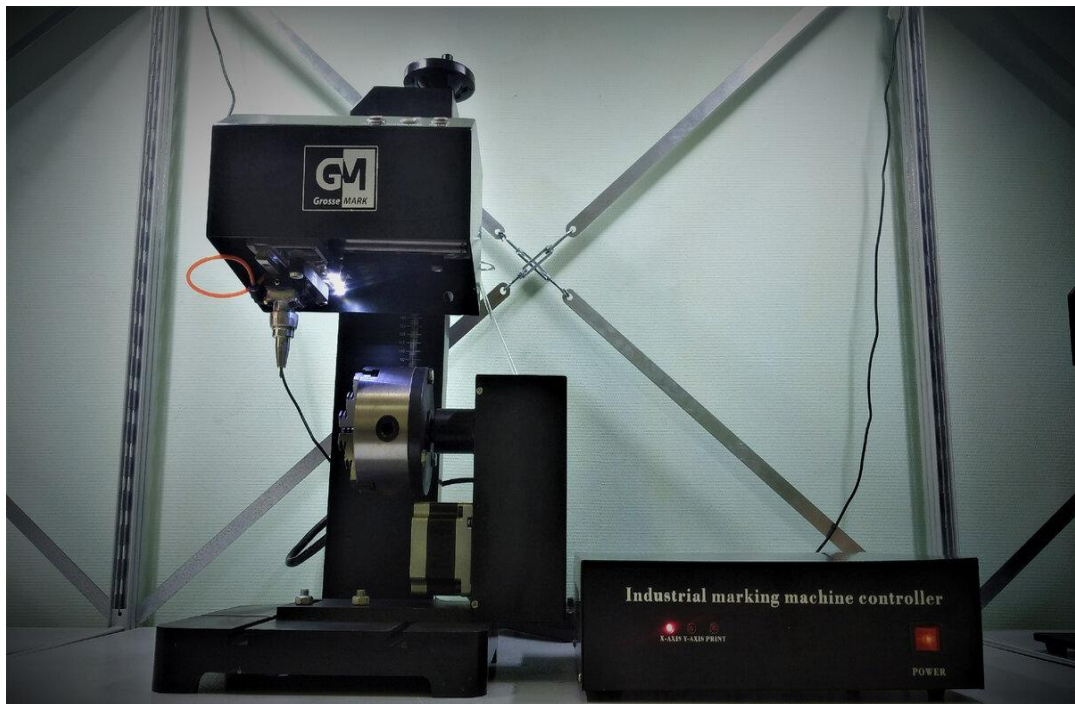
Стационарний пневматичний ударно-крапковий маркіратор MARK-TECH 025
